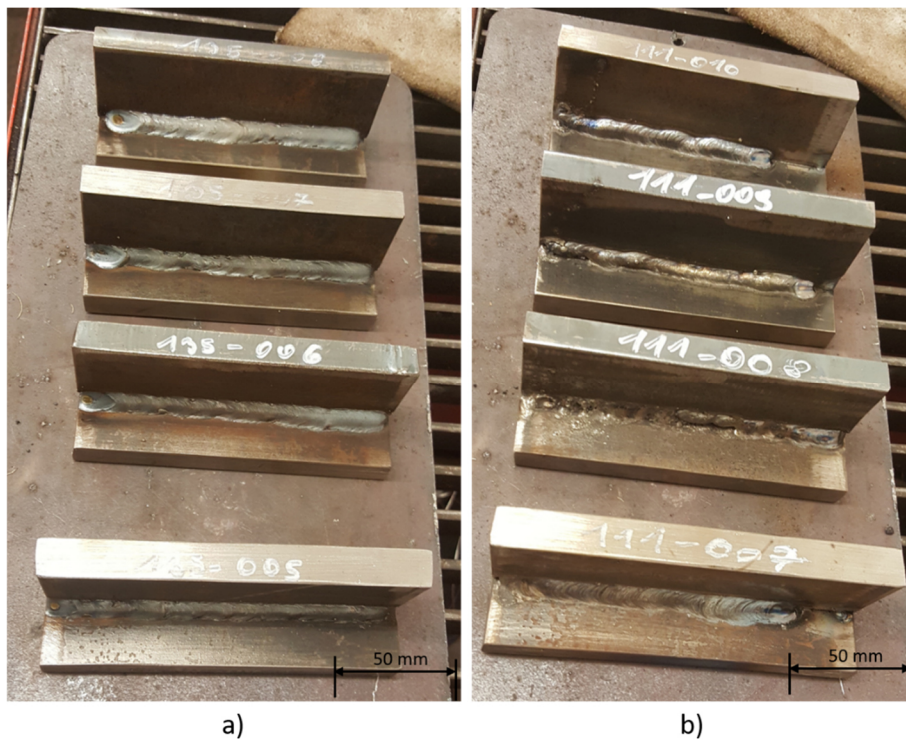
Durchgeführte Kehlnahtschweißungen a) Elektrodenhandschweißen; b) Metall Aktivgasschweißen
